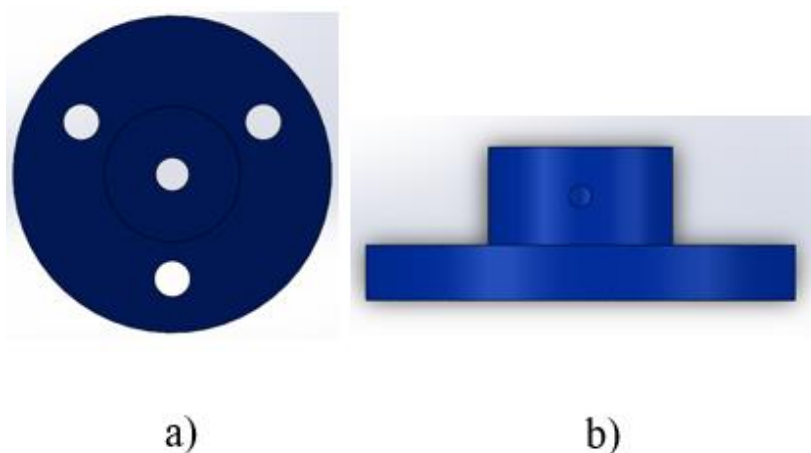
Acople motor/rueda a) Vista frontal b) Vista superior
